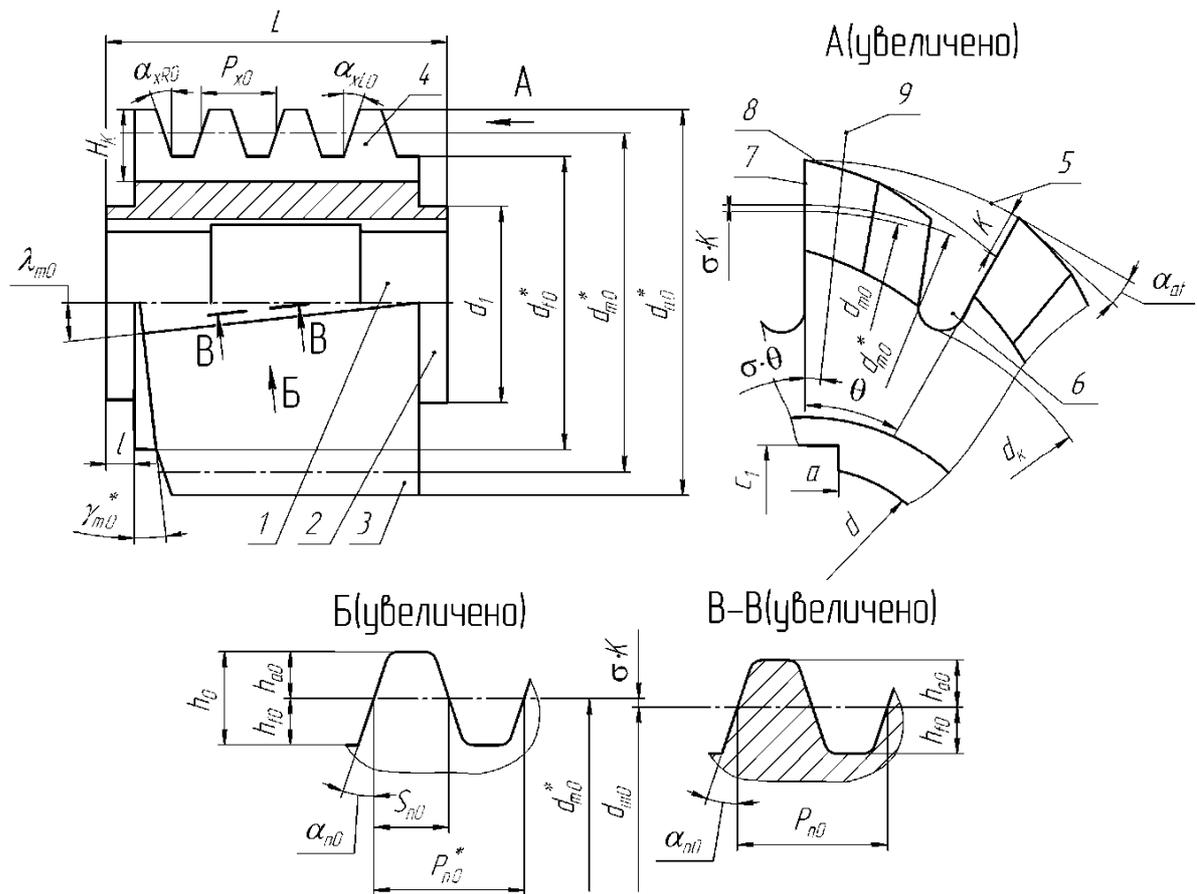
Однозаходная червячная зуборезная фреза (ГОСТ 9324-80) для окончательной обработки цилиндрических колес с эвольвентным профилем:
